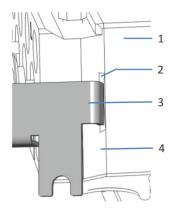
Entfernen der Hinterspülplatte mit dem Abstandswerkzeug
